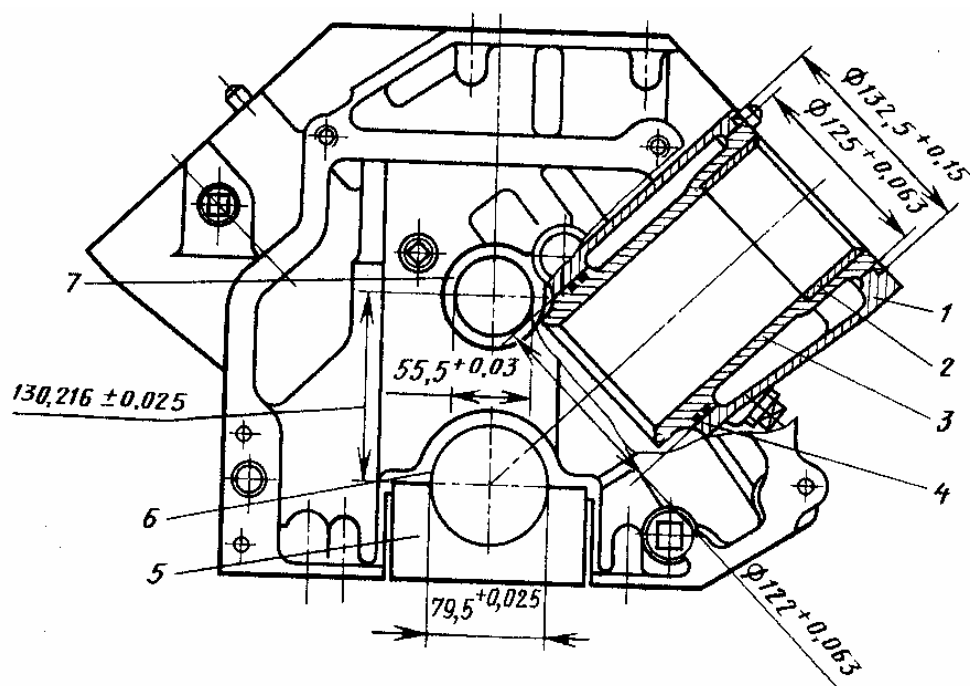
Корпусная сборочная единица «блок цилиндров с гильзами и втулками» двигателя внутреннего сгорания с рабочим объемом 5,5 л: 1 – блок цилиндров; 2 – вставка гильзы; 3 – гильза цилиндра; 4 – уплотнительное кольцо; 5 – крышка коренного подшипника; 6 – поверхность коренной опоры; 7 – втулка распределительного вала
